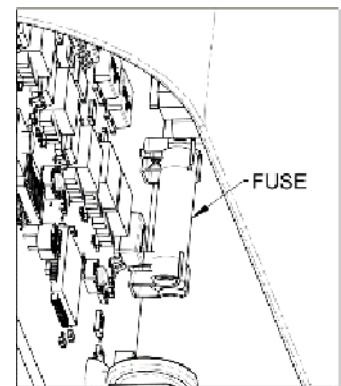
Remplacement du fusible vu depuis le dessous du bol
